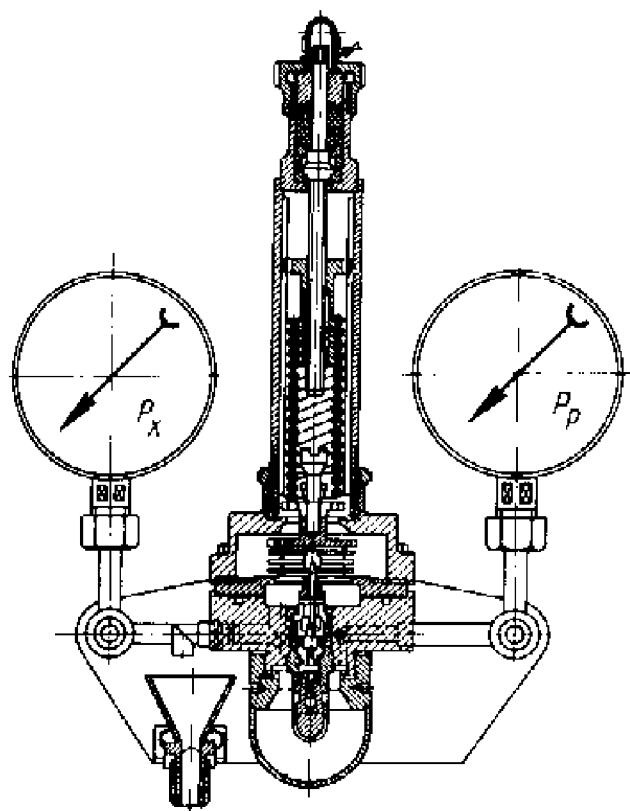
Регулирующий прибор РД-3а односильфонной сборки
